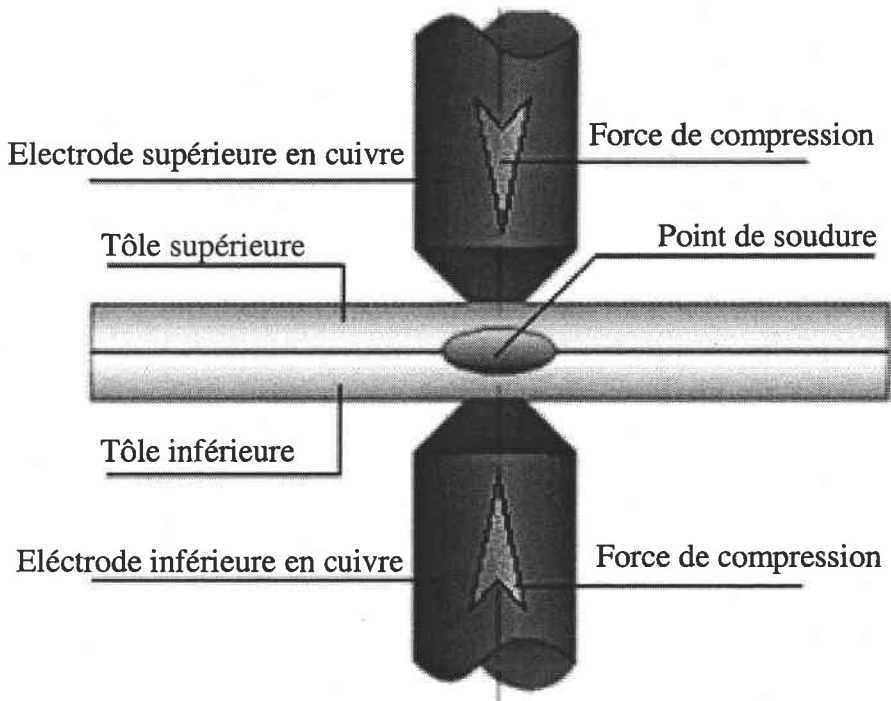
Schéma de l'électrode appliquée pour soudure des joints soudés par point.
